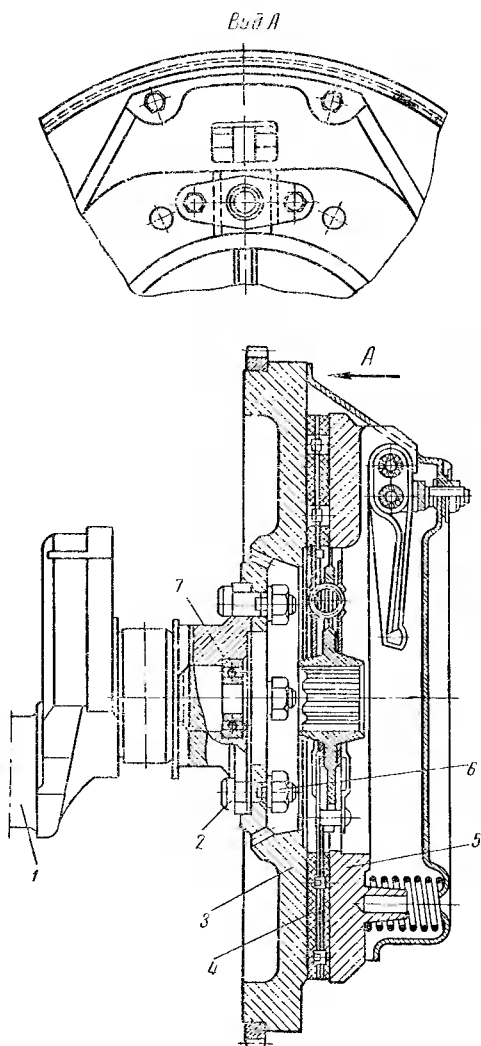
Детали, входящие в сборочный узел (коленчатый вал с маховиком и сцеплением в сборе):
